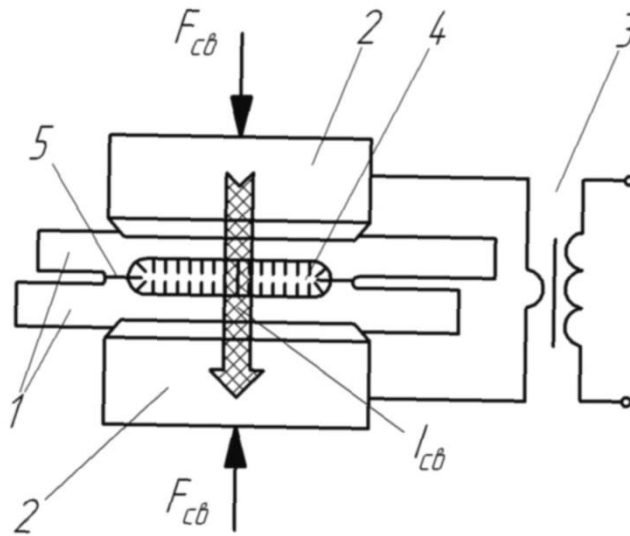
Схема выполнения контактной точечной сварки
